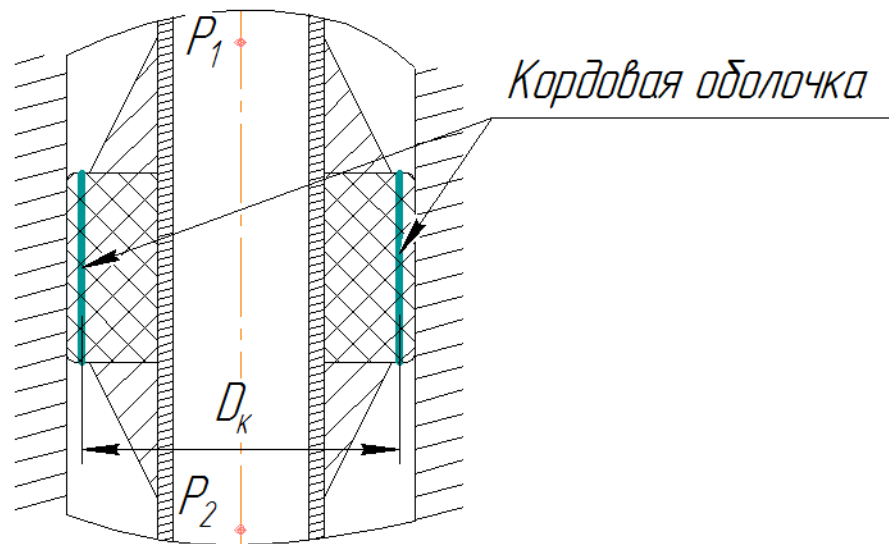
Резиновый уплотнительный элемент с кордовой оболочки в распакерованном положении
